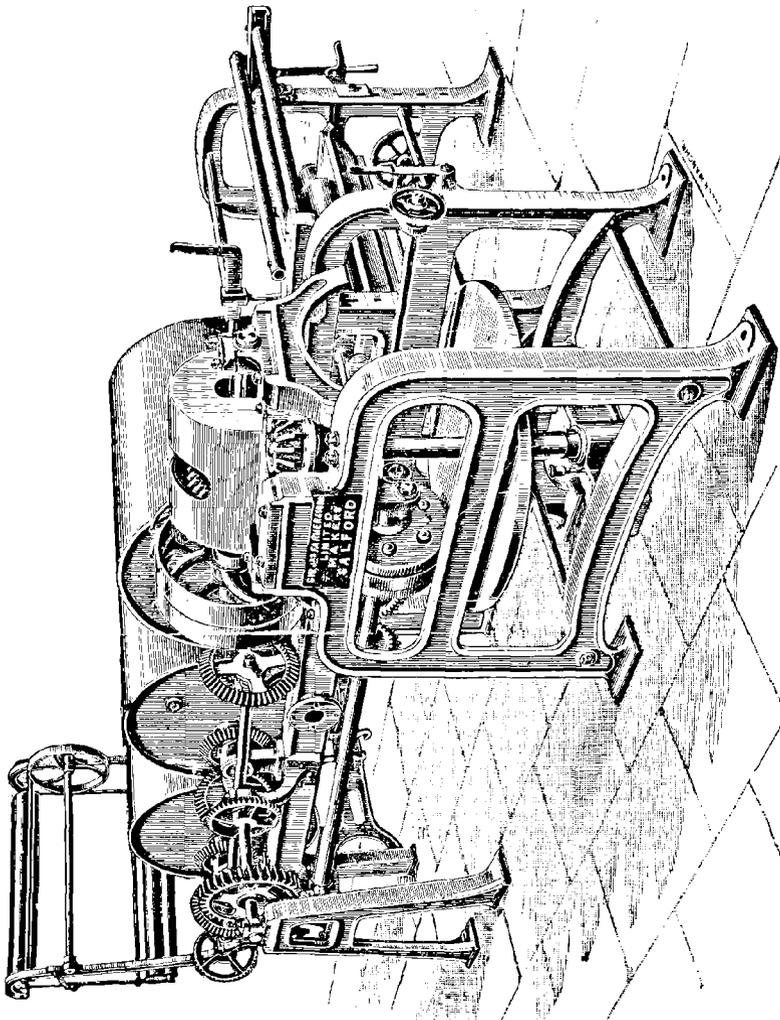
Tambour à 3 cylindres (Il ne se fait que pour une largeur de pièces).
